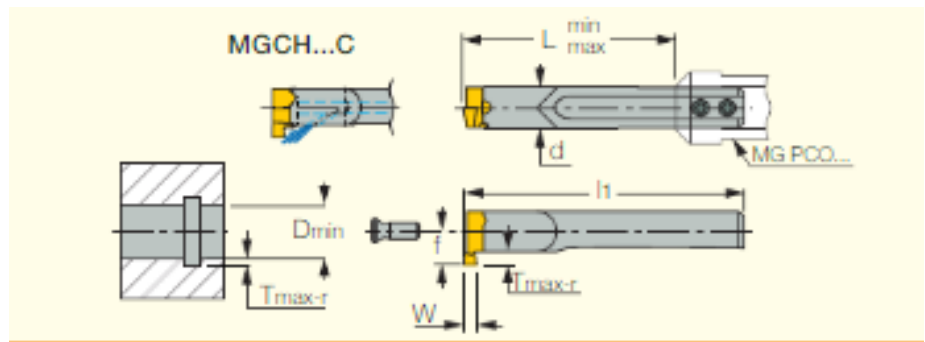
Державка MGCH 06 и пластинка GIQR/L 8-2.00-0.1
